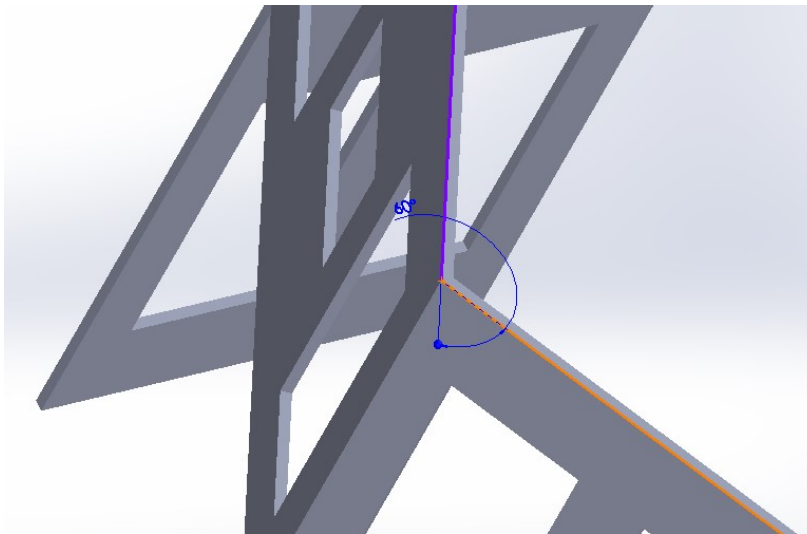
Ensamblaje placa frontal con frontal-lateral
